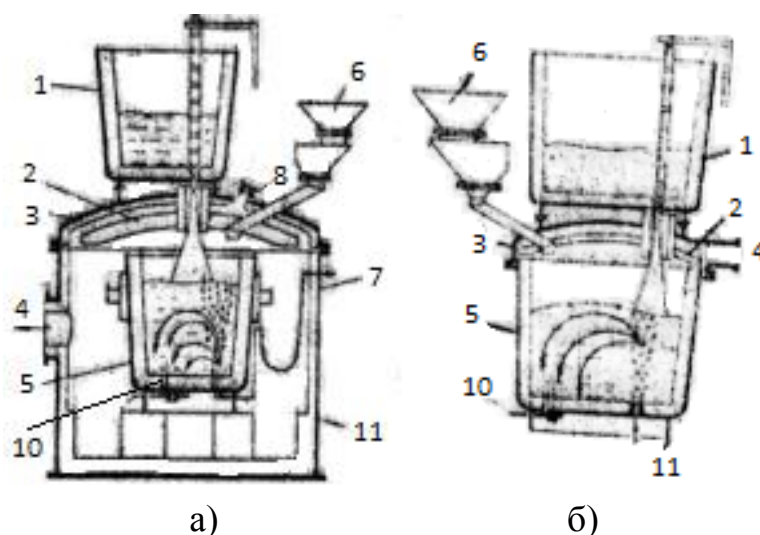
Обработка стали струйным вакуумированием при переливе из ковша в ковш с использованием вакуумной камеры (а) и без нее (б): 1 - первый сталеразливочный ковш; 2 – защитный экран; 3 – крышка вакуумной камеры (ковша); 4 – патрубок к вакуумным насосам; 5 – второй сталеразливочный ковш; 6 – система подачи легирующих материалов и раскислителей; 7 – вакуумная камера; 8 – гляделка; 10 - шиберный затвор; 11 – подача инертного газа
